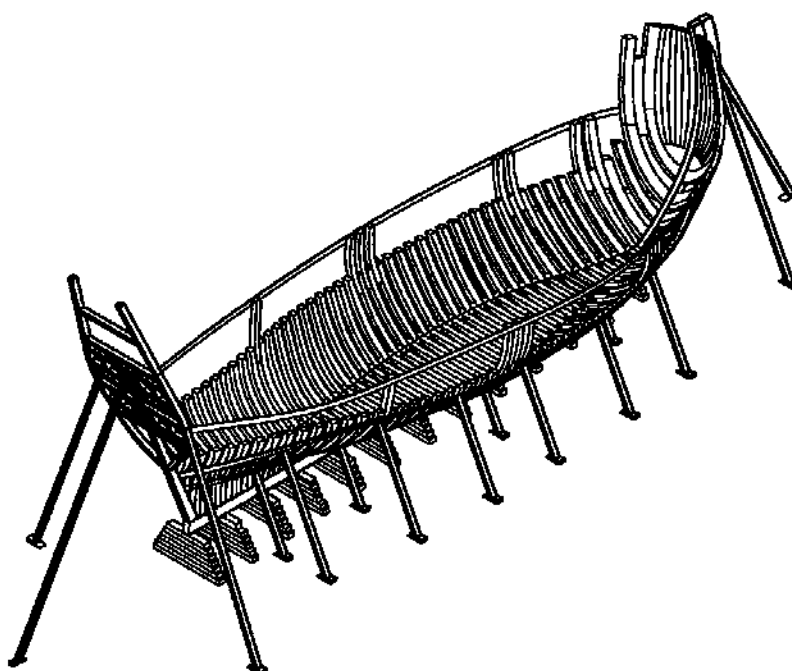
Con la colocación de las estamenaras se llega al nivel de la cubierta principal. A proa se sitúa el horcón o último pique a partir del cual se colocan los espaldones.
